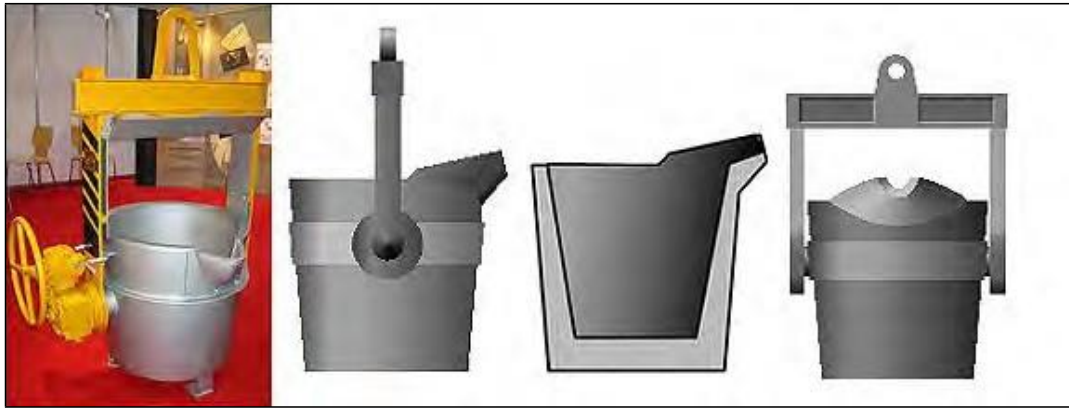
Розливний ківш для заливання розплавленого металу
